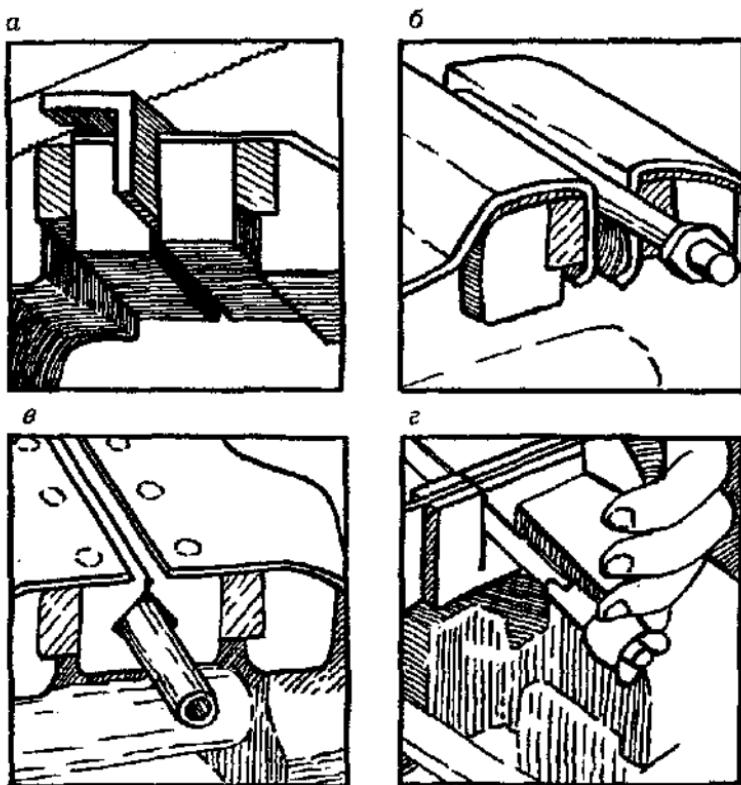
Защитные губки: а — из твердой древесины; б — из алюминия; в — для труб; г — фиксация тонких пластин.
